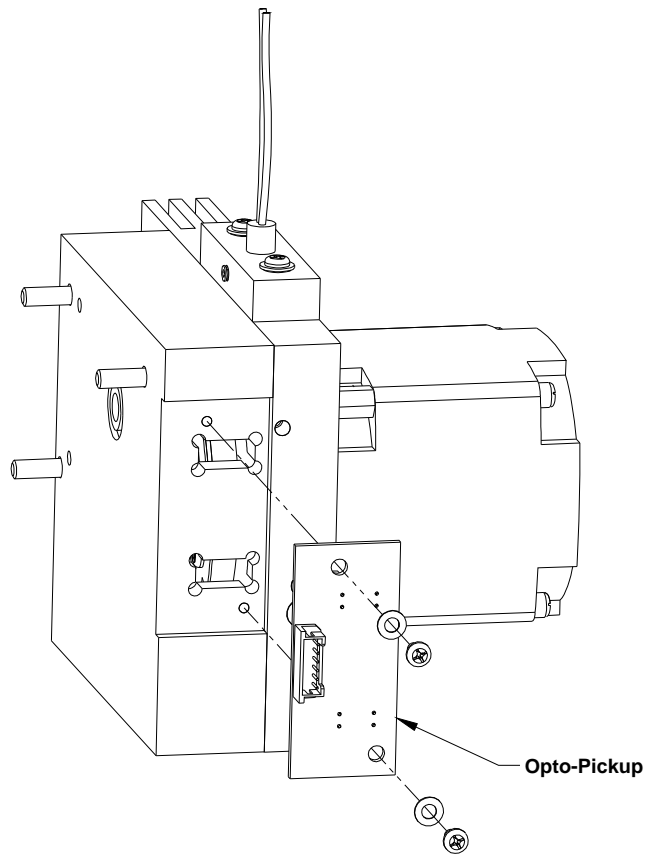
Entfernen der Opto-Pickup Baugruppe
